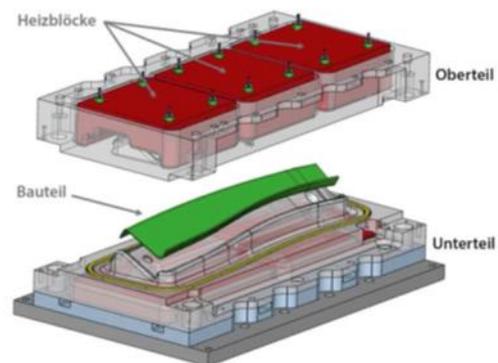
Zweiteiliges Presswerkzeug bestehend aus Basiswerkzeug mit aufgesetzten Formeinsätzen (transparent) (© MBB Fertigungstechnik)
